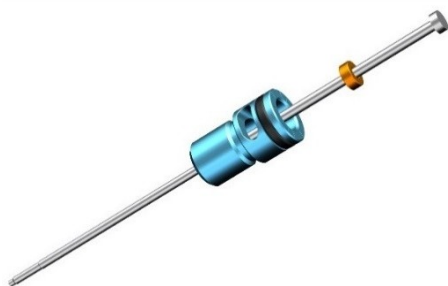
Игольчатый клапан, шайба и держатель иглы
